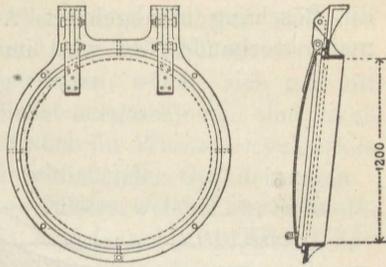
Hängeklappe mit schmiedeeisernem, gewölbtem Deckel.
